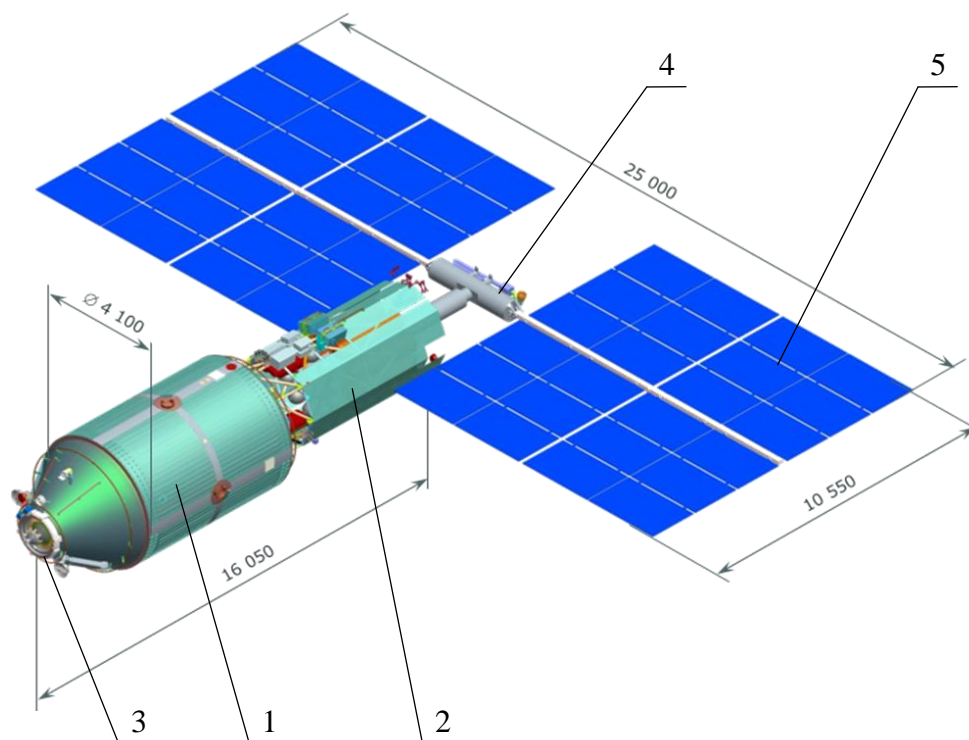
Научно-энергетический модуль: 1 – корпус герметичный; 2 – корпус негерметичный; 3 – стыковочный агрегат; 4 – механизм поворота солнечных батарей; 5 – солнечные батареи
